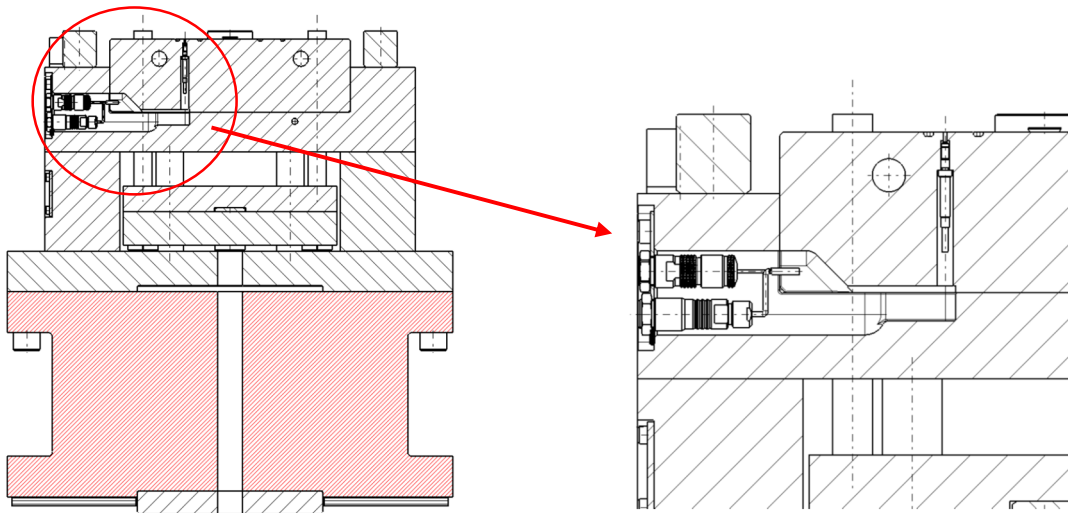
Kabelkanal und Bohrung für den Drucksensor im Schnitt
